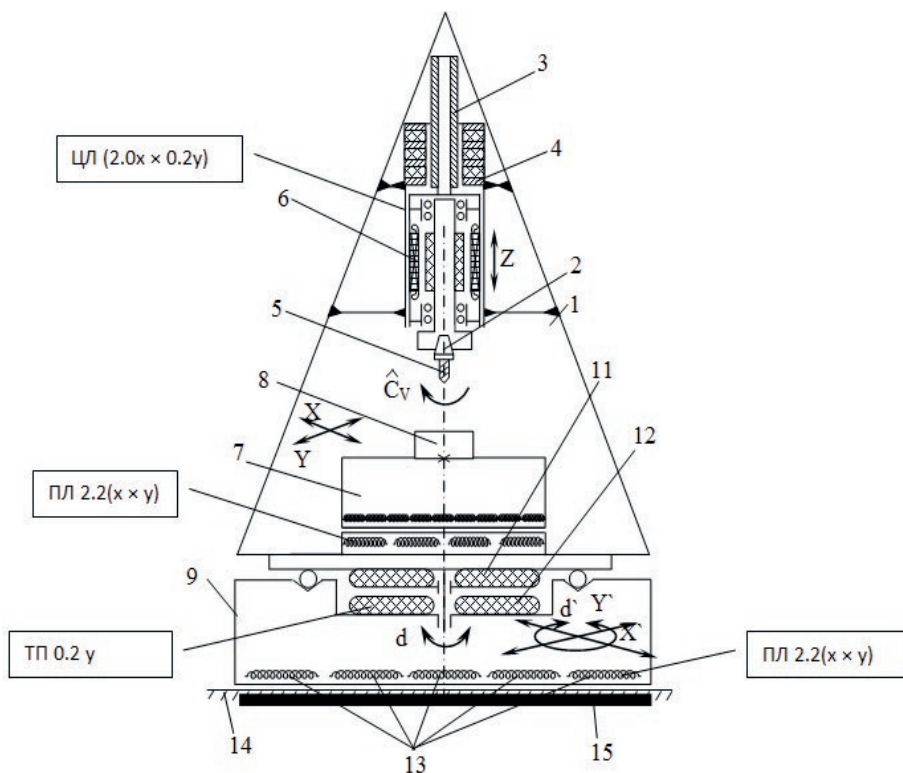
Багатокоординатний мобільний свердлильно-фрезерний верстат майбутнього без механічних передач із генетичними формулами
